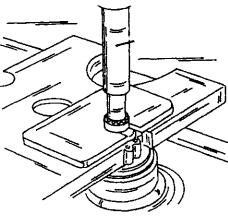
Запрессовывание упорного кольца над стопорным кольцом вала якоря.
